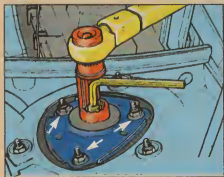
Верхняя опора амортизатора "Ауди-100". Стрелки показывают гайки и шайбы крепления пластины.
